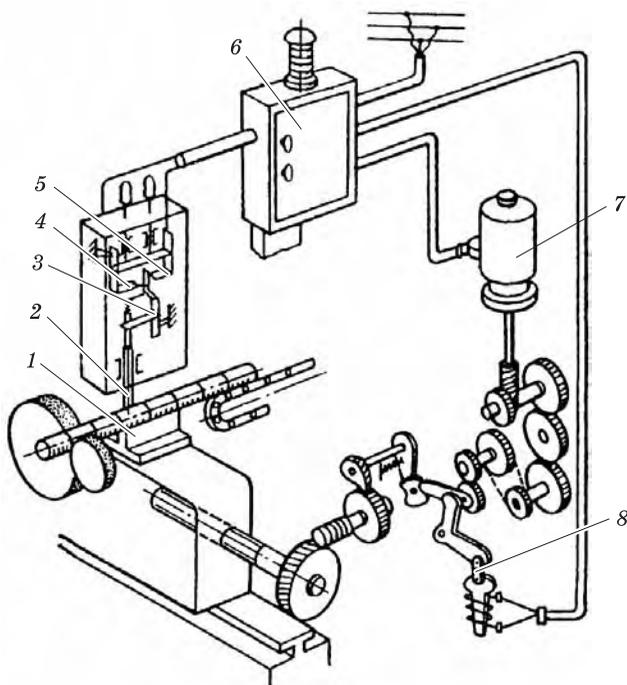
Схема устройства активного контроля бесцентрово-шлифовального станка
